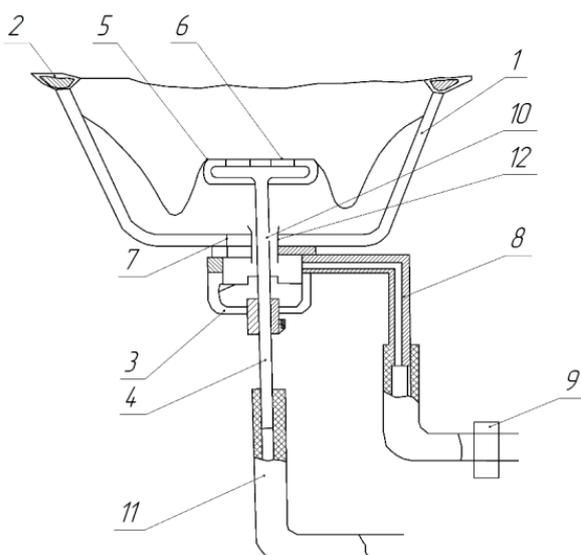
Схема устройства для массажа вымени животных, выполненного по варианту В-2: 1 – кожух; 2 – уплотняющий элемент; 3 – пневмокамера; 4 – шток; 5 – присосок; 6 – крышка; 7, 10 – калиброванные отверстия; 8 – патрубок; 9 – пульсатор; 11 – шланг; 12 – направляющая
